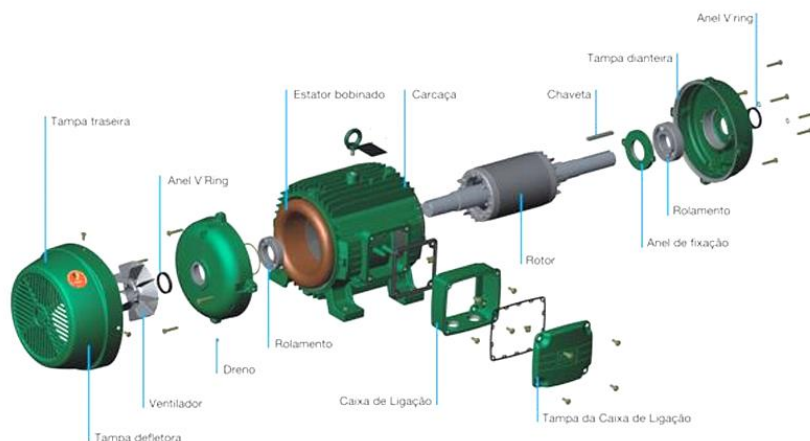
Vista explodida de um motor trifásico de rotor em gaiola.
